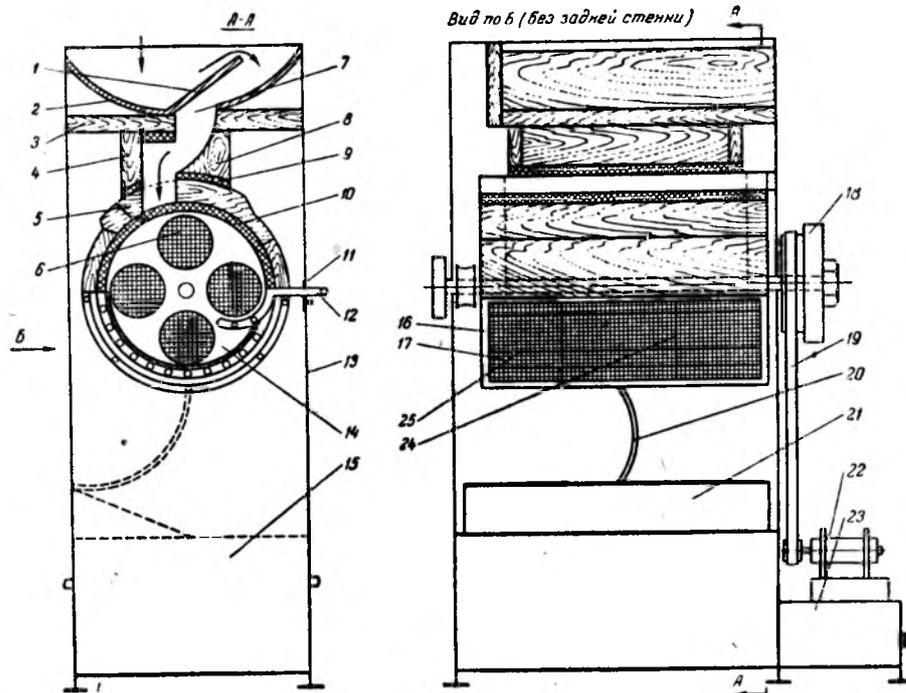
Разрез машины: а) поперечный — по АА; б) продольный — по Б (без задней стенки)
